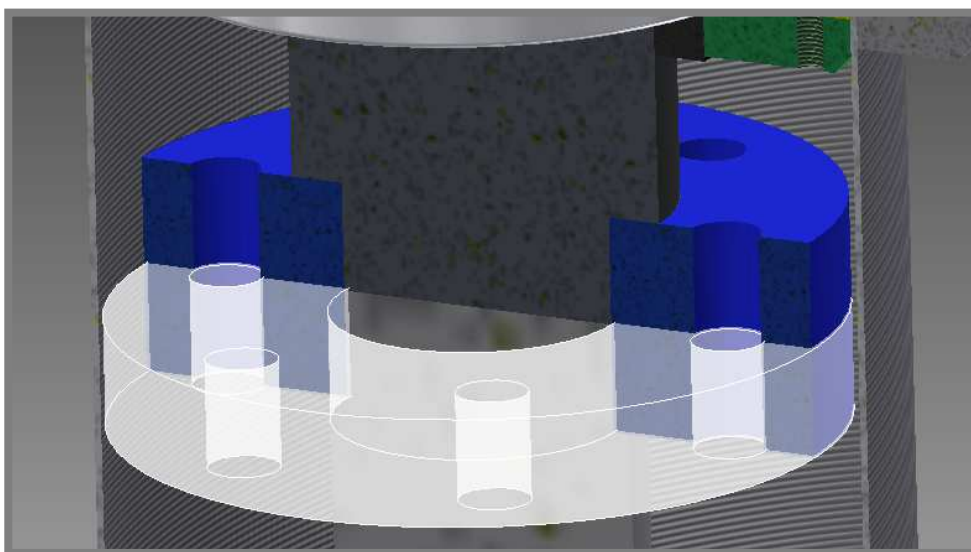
Detail konstrukčního řešení 3 (Kluzné pouzdro 2)
